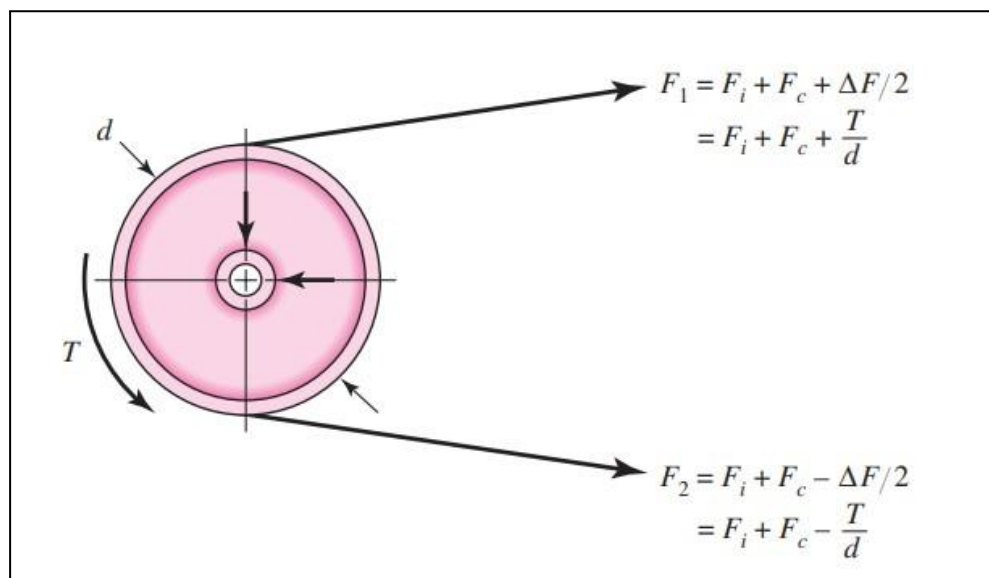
Fuerzas desarrolladas sobre cadenas metálicas. [45].
